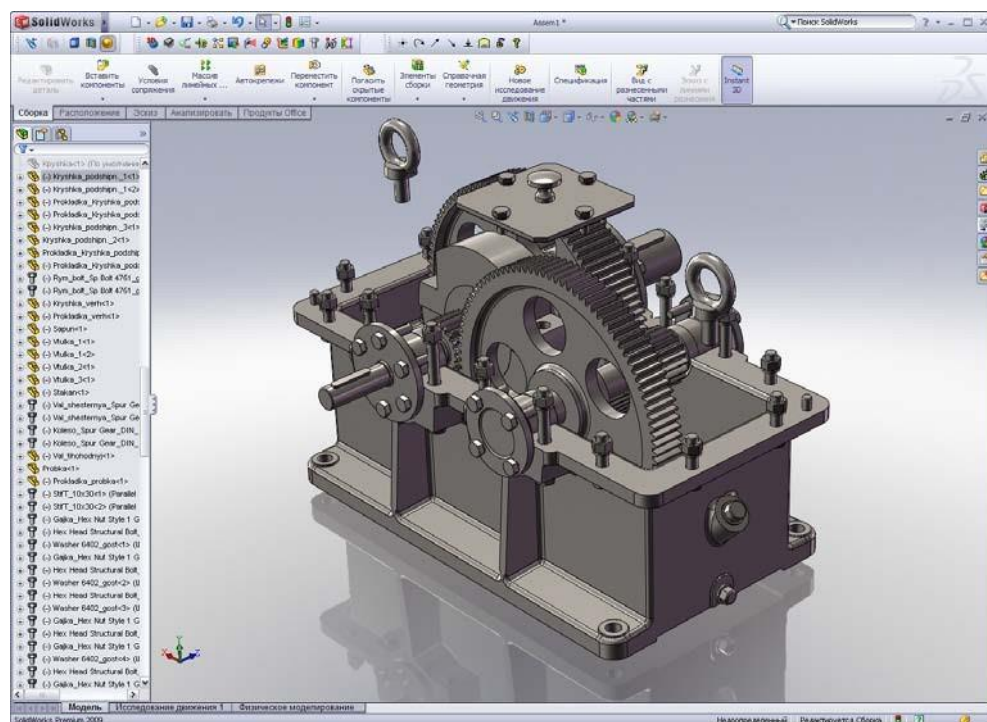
Редагування збірки (верхня кришка редуктора для наочності прихована)
